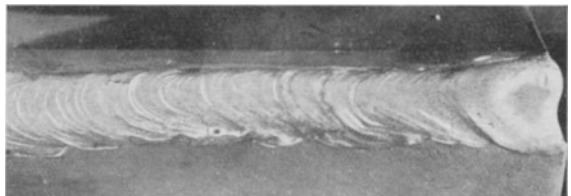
Ecknaht (Kehlnah) an 3 mm-Aluminiumblech.
